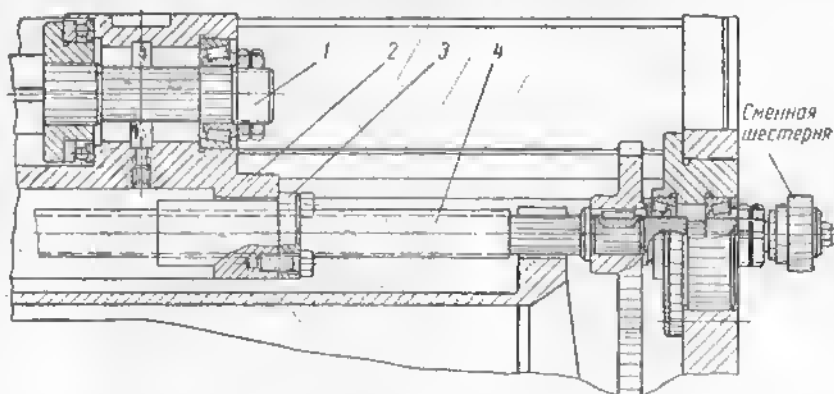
Устройство коробки скоростей и шпиндельное устройство горизонтально-расточного станка 262Г.
